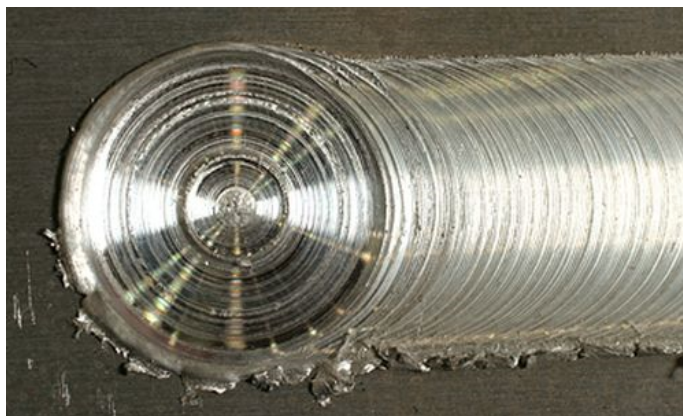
Фрагмент зварного шва ЗТП на алюмінієвій пластині
